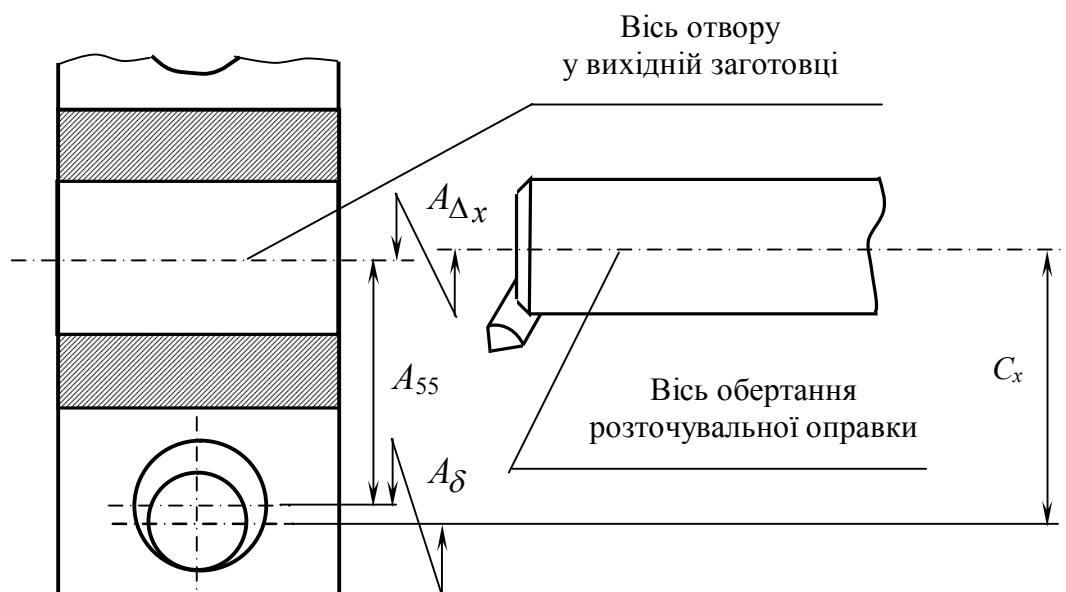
Схема розмірного ланцюга для визначення похибки базування у напрямі осі X
